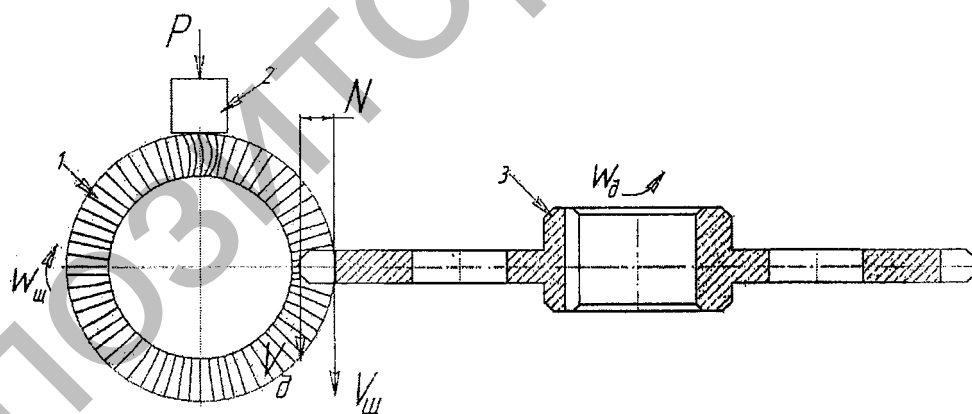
Схема нанесения покрытия вращающейся металлической щеткой на поверхности зубьев звездочек цепных передач: 1 – вращающаяся металлическая щетка; 2 – брусок из материала покрытия; 3 – деталь; P – усилие прижатия бруска; $V_{щ}$ – линейная скорость вращения щетки; $V_{д}$ – линейная скорость вращения детали; $W_{щ}$ – угловая скорость вращения щетки; $W_{д}$ – угловая скорость вращения детали; N – натяг щетки
